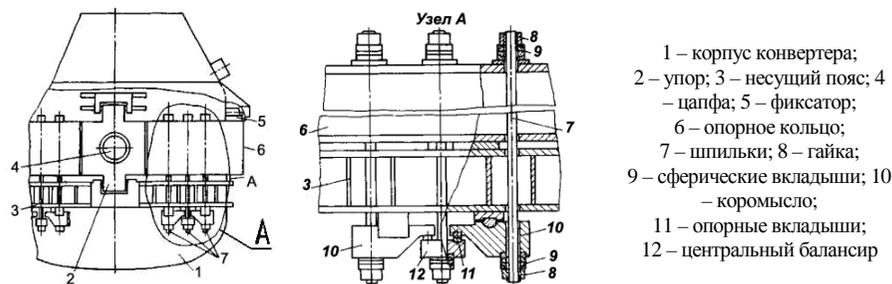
Крепление корпуса в опорном кольце с помощью шпилек
